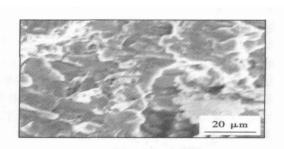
填加 Ti-Ni 合金时接头断口 Fig. 5 Fractograph of welded joint with Ti-Ni alloy
